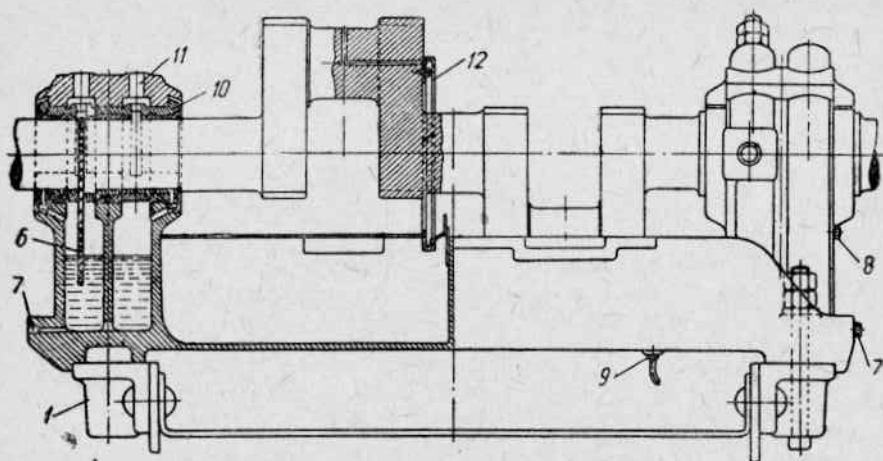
Двухкривошипный вал Людиновского завода. 1—угольник для крепления опорного блока вала, 2—распорная втулка, 3—болты, крепящие опорный блок, 4—нарезные гнезда для стержней, связывающих опоры вала с цилиндрами, 5—крепящие ребра, 6—смазывающая цепь, 7—спускная пробка для масла, 8—проверочная пробка для уровня масла, 9—пробка для спуска масла из опорного блока, 10—вкладыши, 11—смотровые отверстия для проверки смазочных цепей, 12—кольцо для центробежной смазки шейки кривошипа, 13—крышечные болты.
